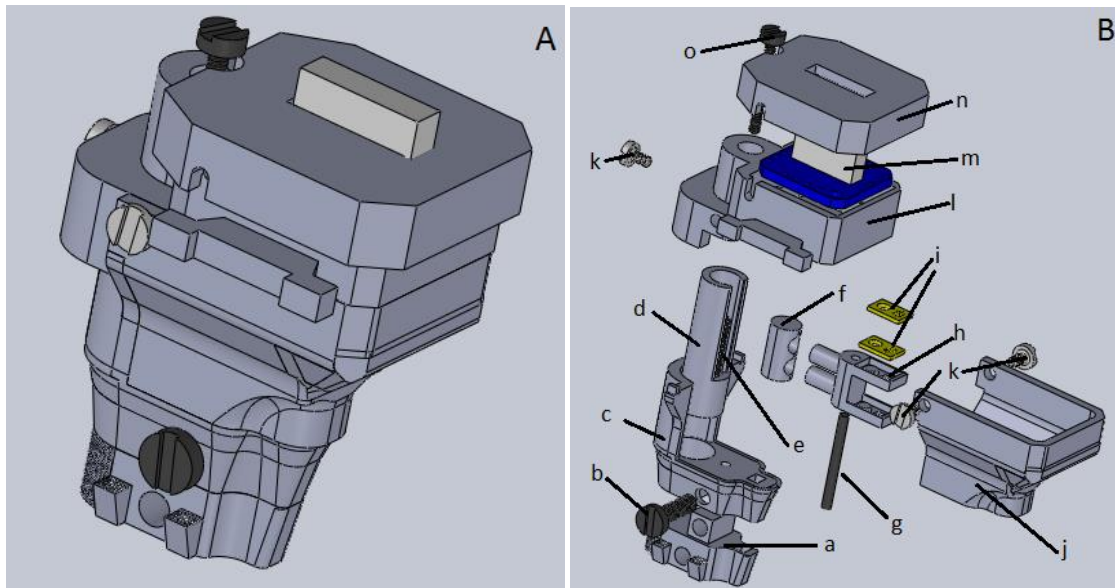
Diseño Final. (A) Vista isométrica. (B) Vista explosiva.
